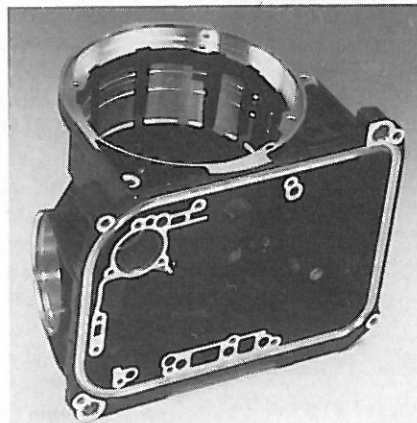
Getriebegehäuse aus GD-AlSi 12 Cu
